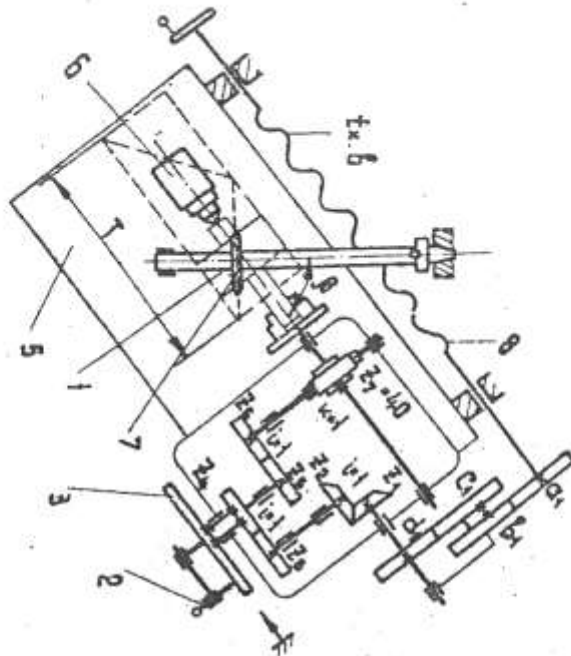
Кінематична схема універсальної ділянової головки настроєної на обробку зубчастих коліс з гвинтовим зубом:
